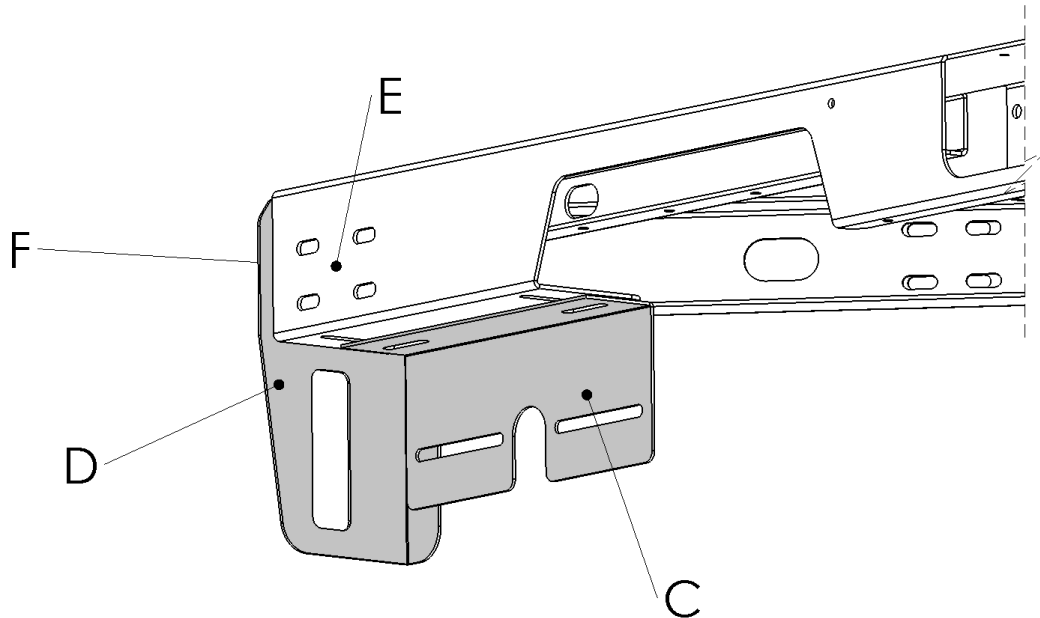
d Staffe di montaggio, regolazione e protezione delle luci posteriori
